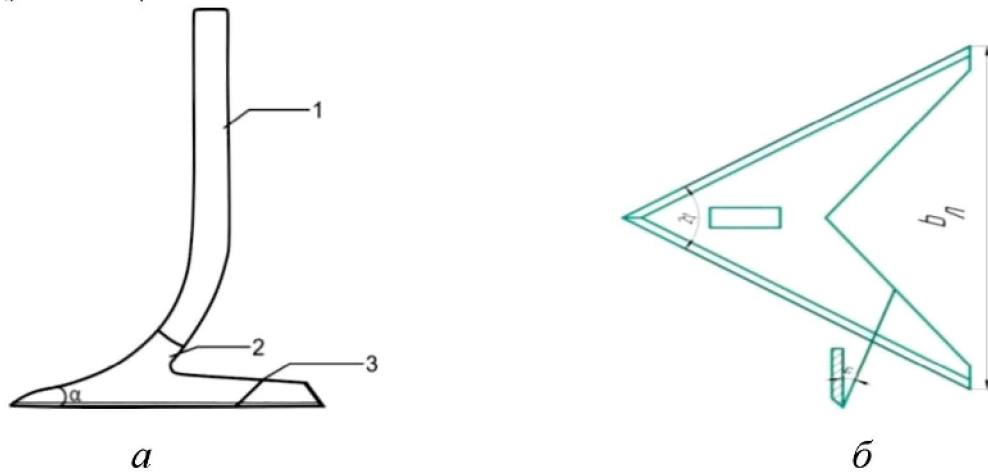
Схема стрілкової лапи: а - вид збоку; б - вид зверху,
